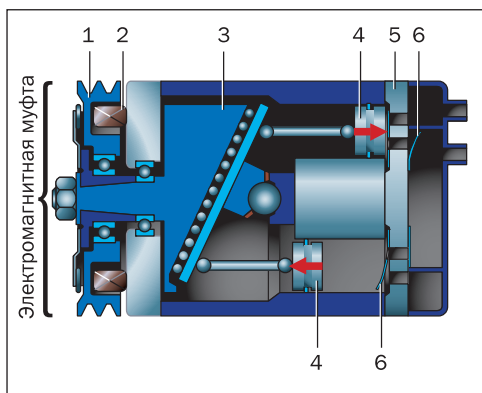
Схема компрессора автомобильного кондиционера: 1 — шкив; 2 — электромагнит; 3 — наклонная шайба; 4 — поршень; 5 — крышка блока цилиндров; 6 — клапаны
